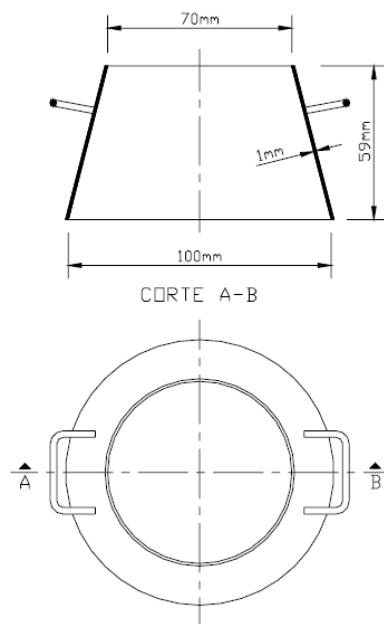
Cone para ensaio de espalhamento em argamassas
